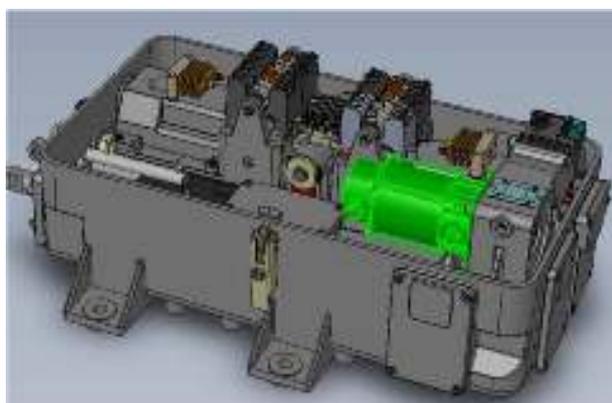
Двигатель стрелочного электропривода типа Р80
